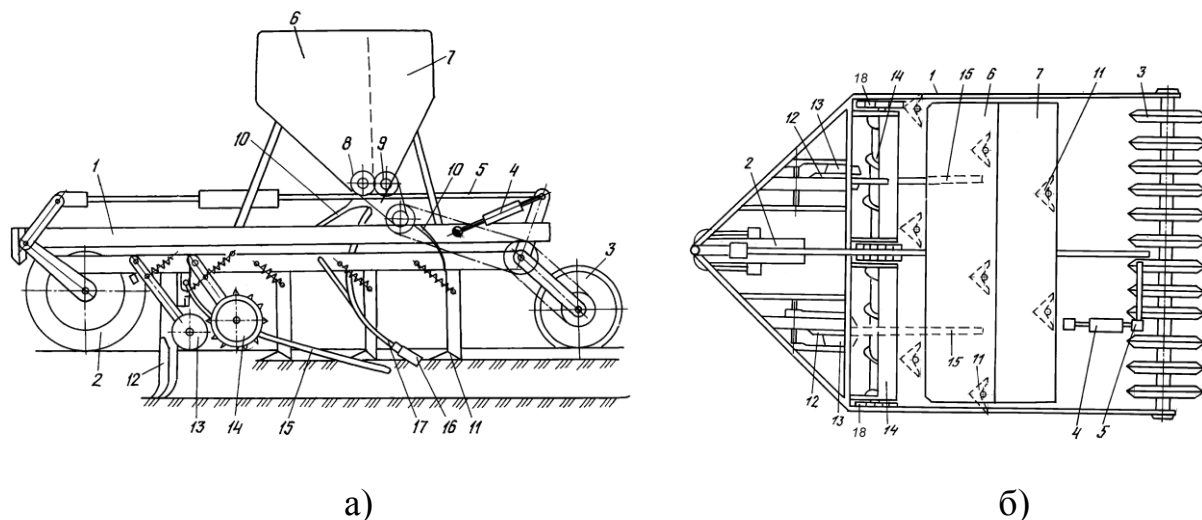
Комплексный почвообрабатывающий агрегат (а – сбоку; б – сверху): 1 – рама; 2 – переднее самоустанавливающееся колесо; 3 – катки; 4 – гидросистема; 5 – рычажные механизмы; 6 – семенной бункер; 7 – туковый бункер; 8 – аппараты для высева семян; 9 – туковысевающие аппараты; 11 – лаповые сошники; 12 – щелерезы; 13 – конусные катки; 14 – соломонаправители; 15 – соломозаталкиватели; 16 – наконечники; 17 – тукопровод; 18 – приводные колеса
